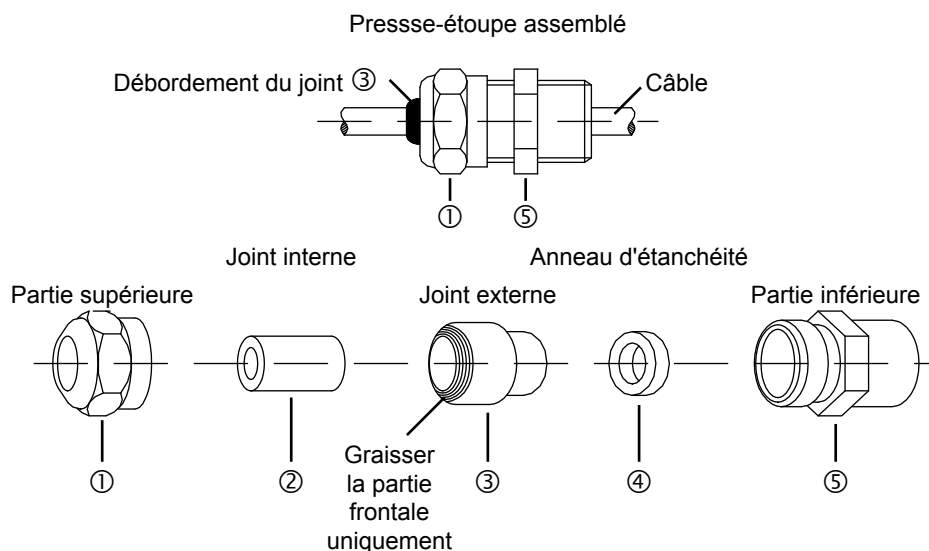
Presse-étoupe (vue d'ensemble et explosée)
